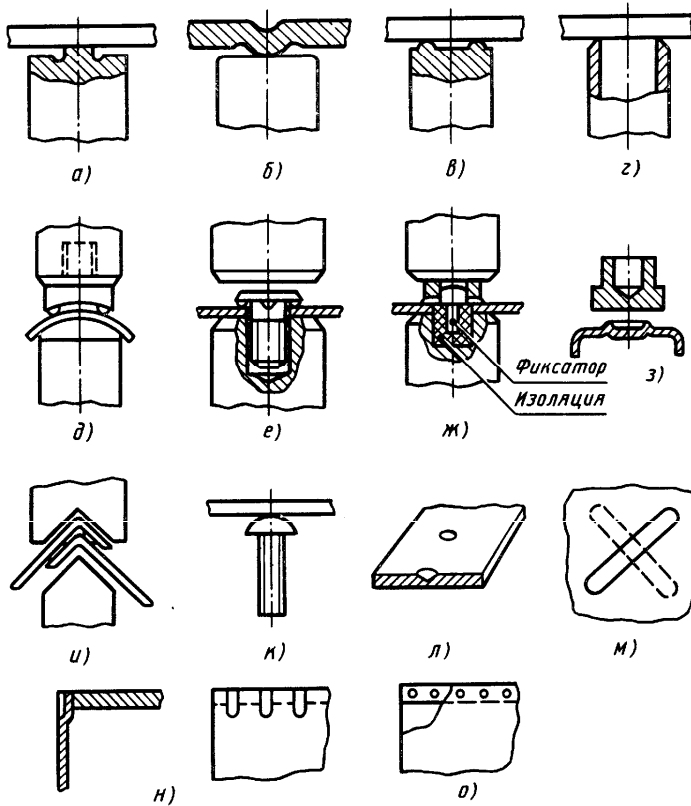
Различные формы выступов, применяемые при рельефной сварке
